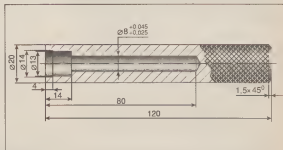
Оправка для напрессовки колпачка на направляющую втулку клапана.
